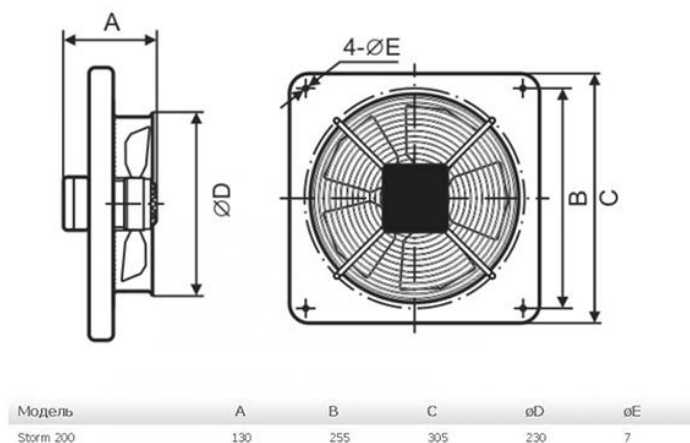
Обозначения габаритных размеров вентилятора
